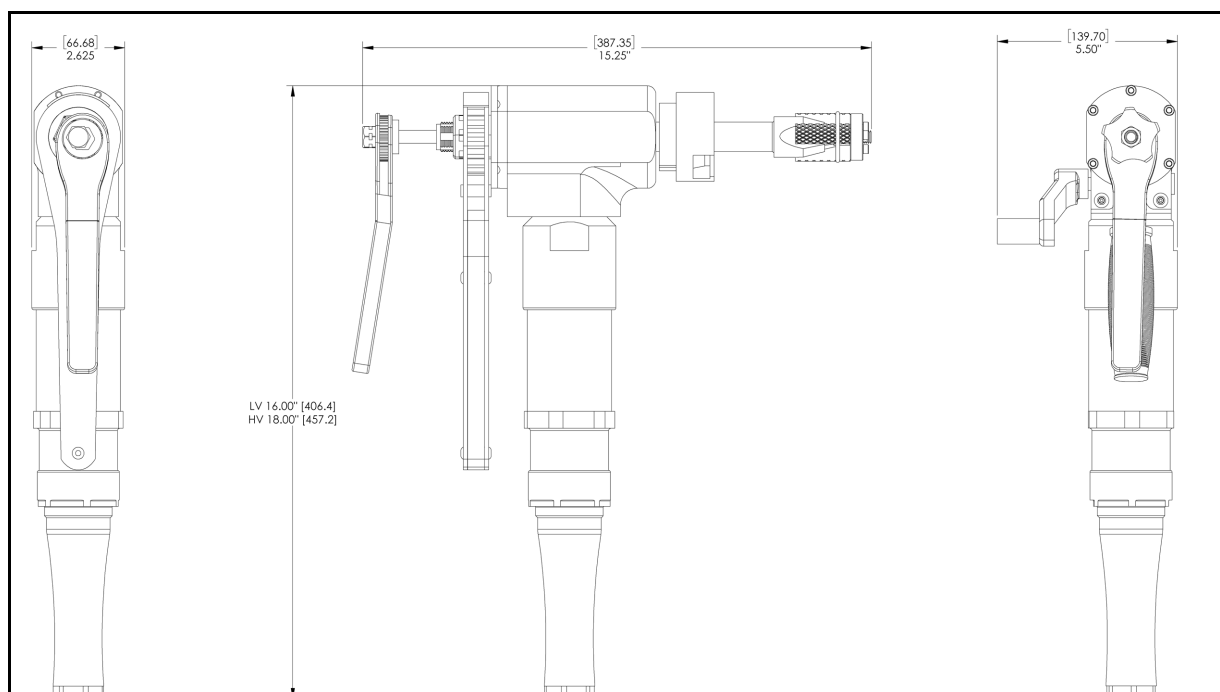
DIMENSIONS DE LA « BOILER GUN » BG44 PNEUMATIQUE
